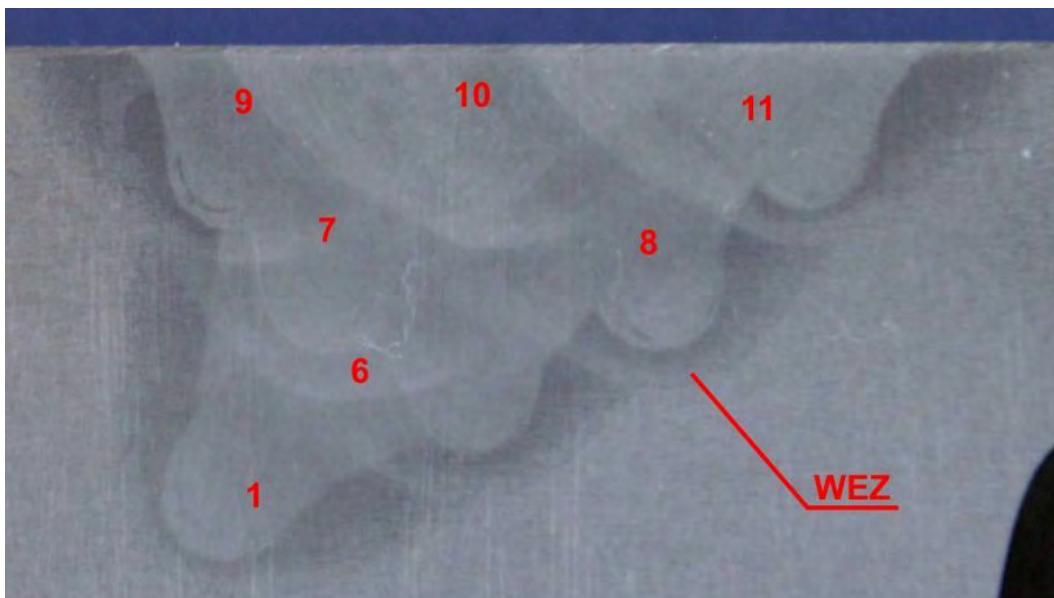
Probe 04 - Ansicht oberer Teil der Schweißnaht
